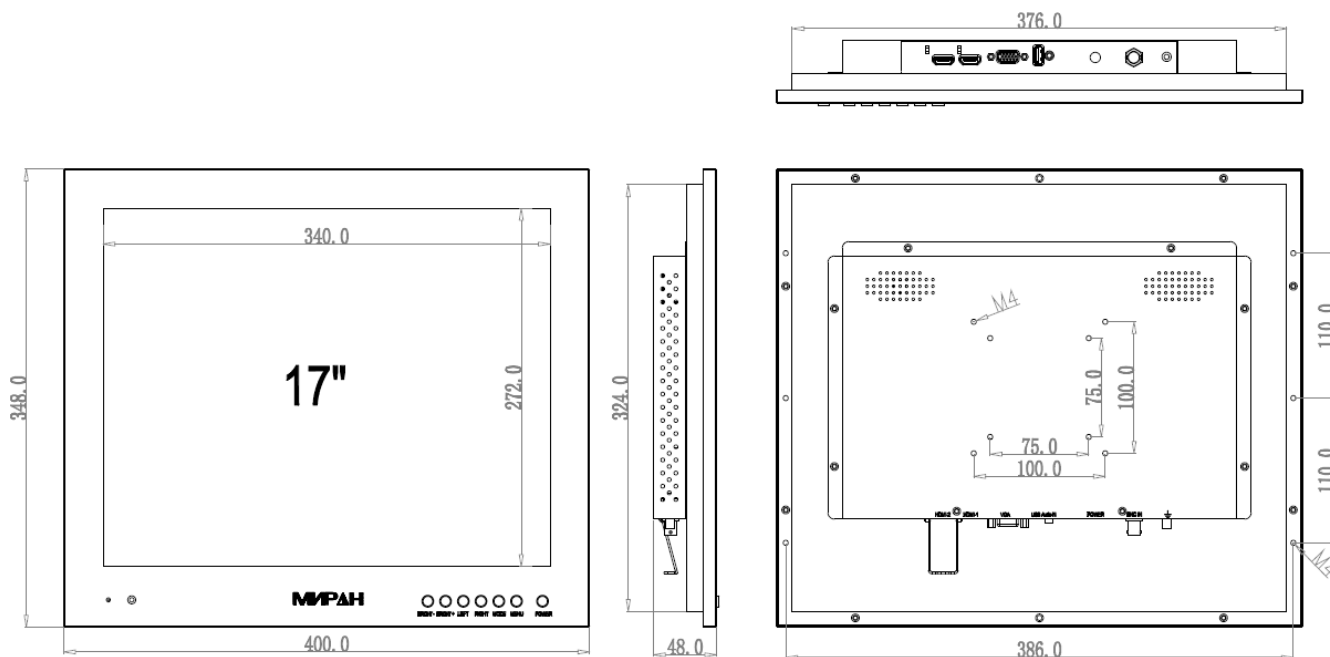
Габаритный чертеж монитора ИВМ-17ЖК.
